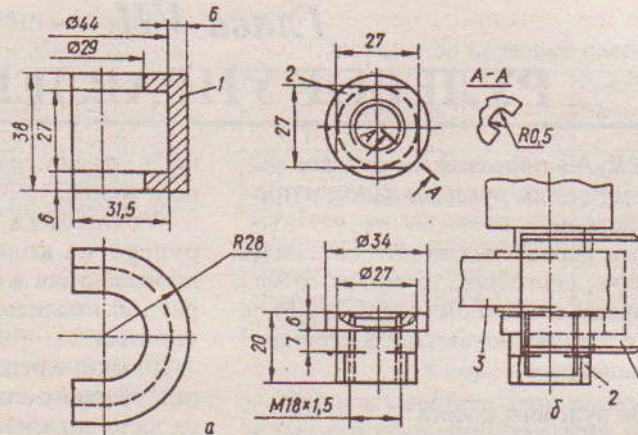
Съемник для снятия сошки рулевого механизма: а - детали съемника; б - установка съемника для снятия сошки; 1 - корпус; 2 - гайка; 3 - сошка
